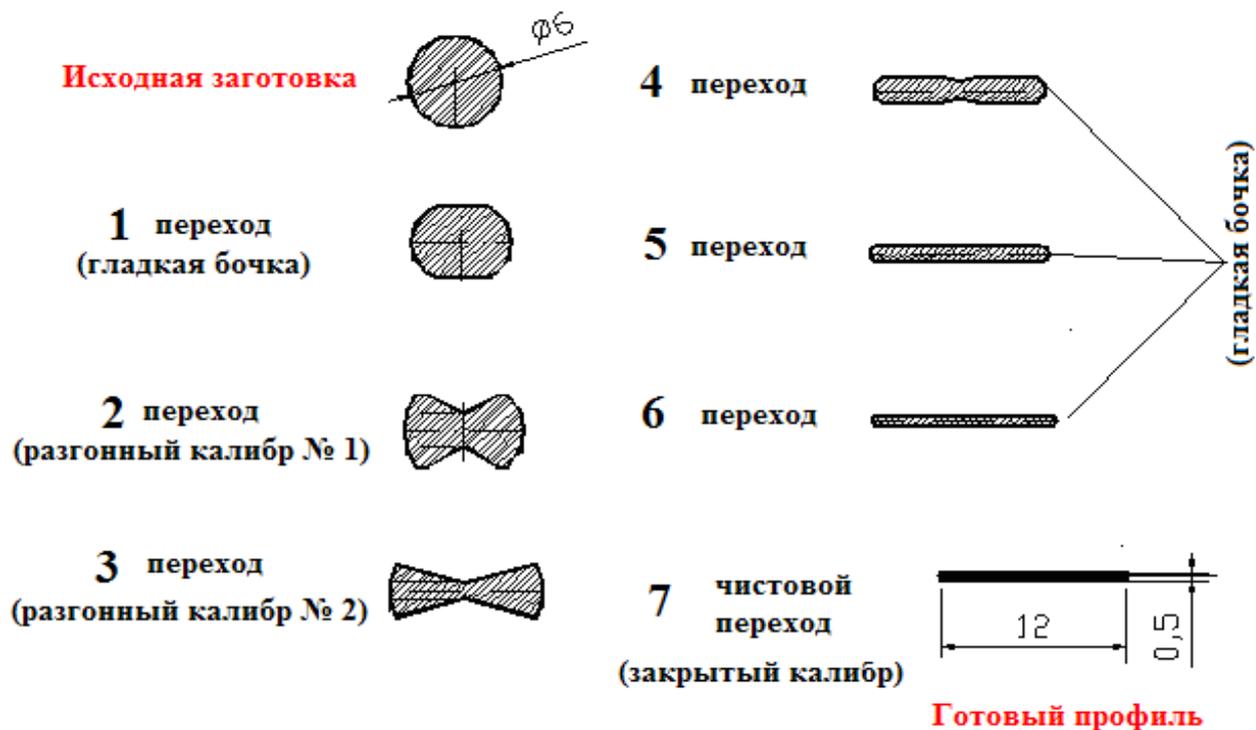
Разработанная калибровка получения ленты сечением $0,5 \times 12,0$ мм из круглой заготовки диаметром 6,0 мм
